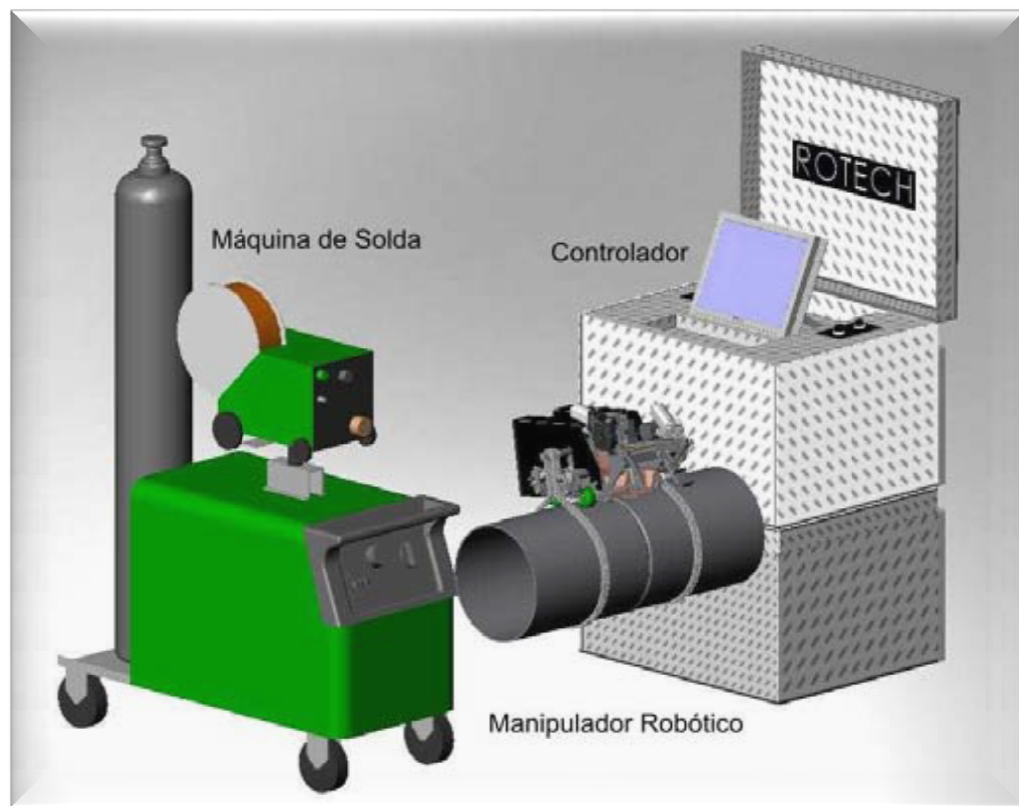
Sistema de robot para soldadura orbital de tuberías. Ivanilza Felizardo, Alexandre Queiroz Bracarense , Hernandes Coutinho Fagundes y Flaviano Lopes, (2007). p. 2
